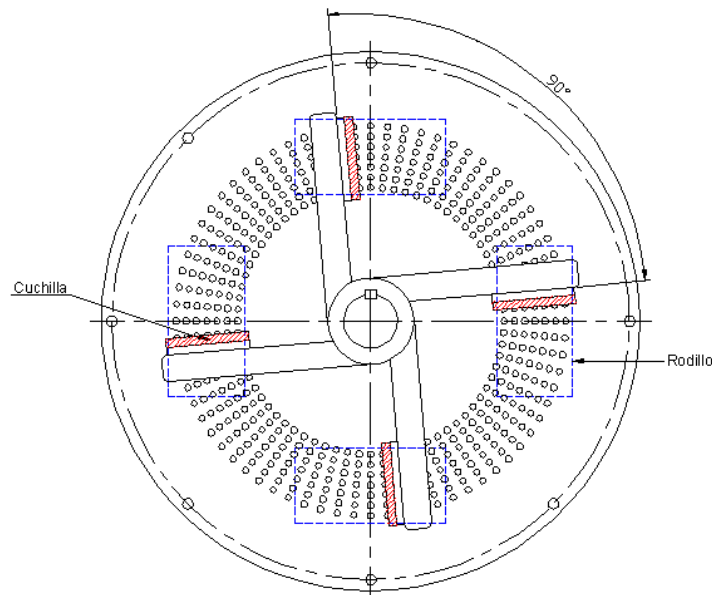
Vista inferior de las 4 cuchillas de corte.
